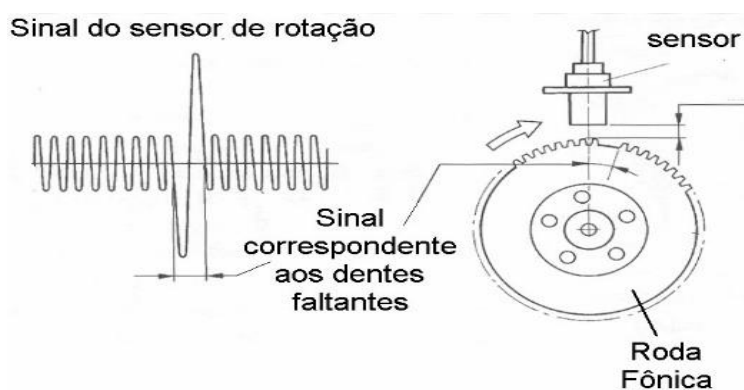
Sinal do Sensor Indutivo em conjunto com roda fônica (Santos,2013)
